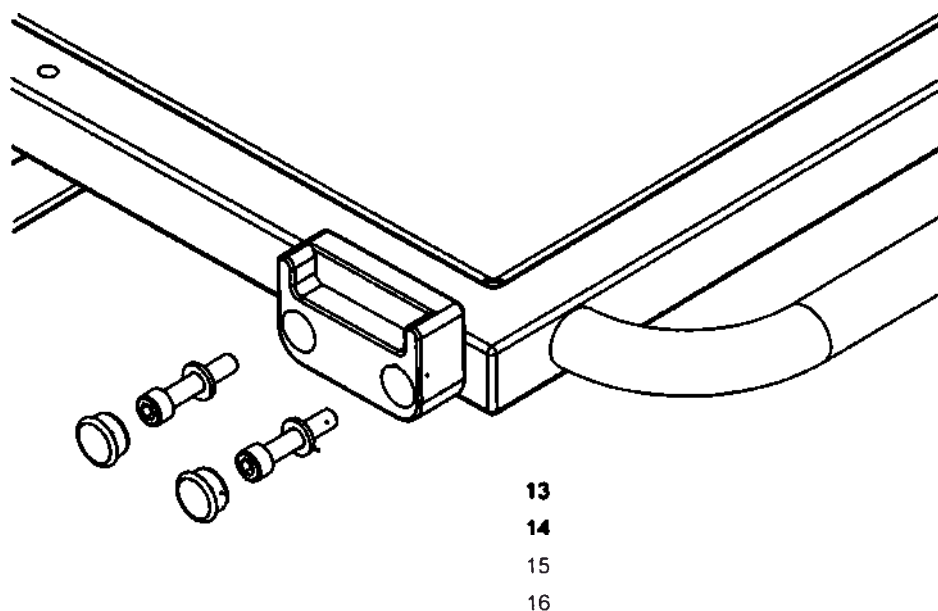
Схема установки опоры для крепления кронштейна К-3.
